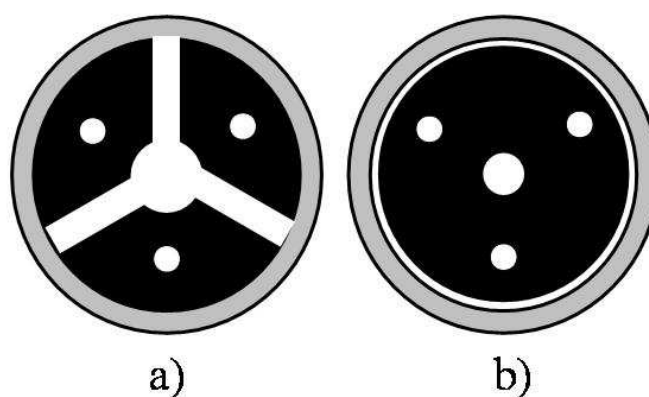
Representação dos sistemas de fixação interna de três pontos (a) e uniforme (b) do anel para o processo de usinagem⁷¹.
